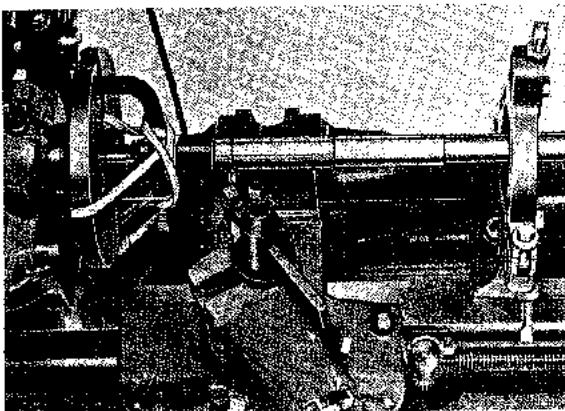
Pieza sujetada contra el punto del cabezal con un cordón de cuero crudo (Sheldon Machine Co., Inc.)
